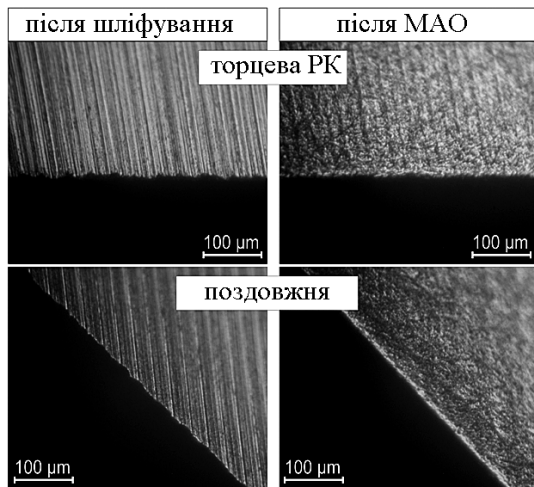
РК кінцевої твердосплавної фрези після шліфування та MAO
